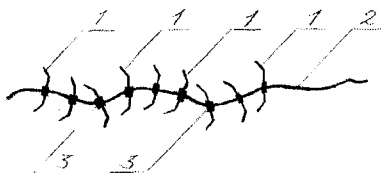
Тарельчатые абразивные пружины, закрепленные на гибком валу: 1 - тарельчатая абразивная пружина; 2 - гибкий вал; 3 - зажимы.
